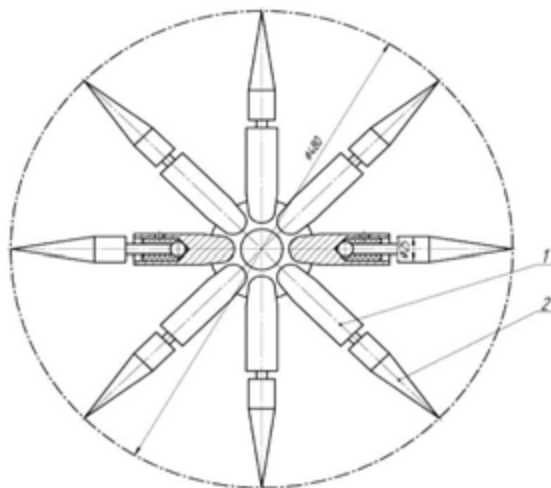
Конструктивна схема біонічного гольчатого диска ротаційної борони
